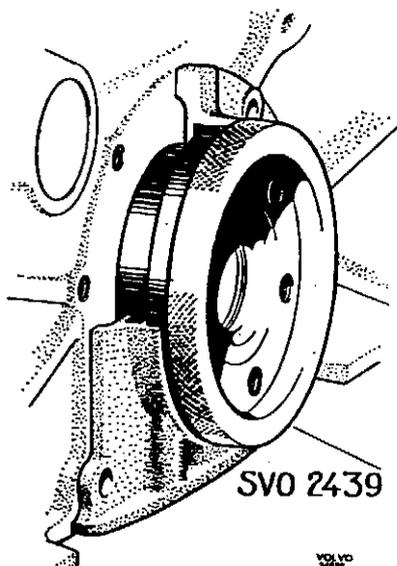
Zentrieren des hinteren Dichtungsflansches
